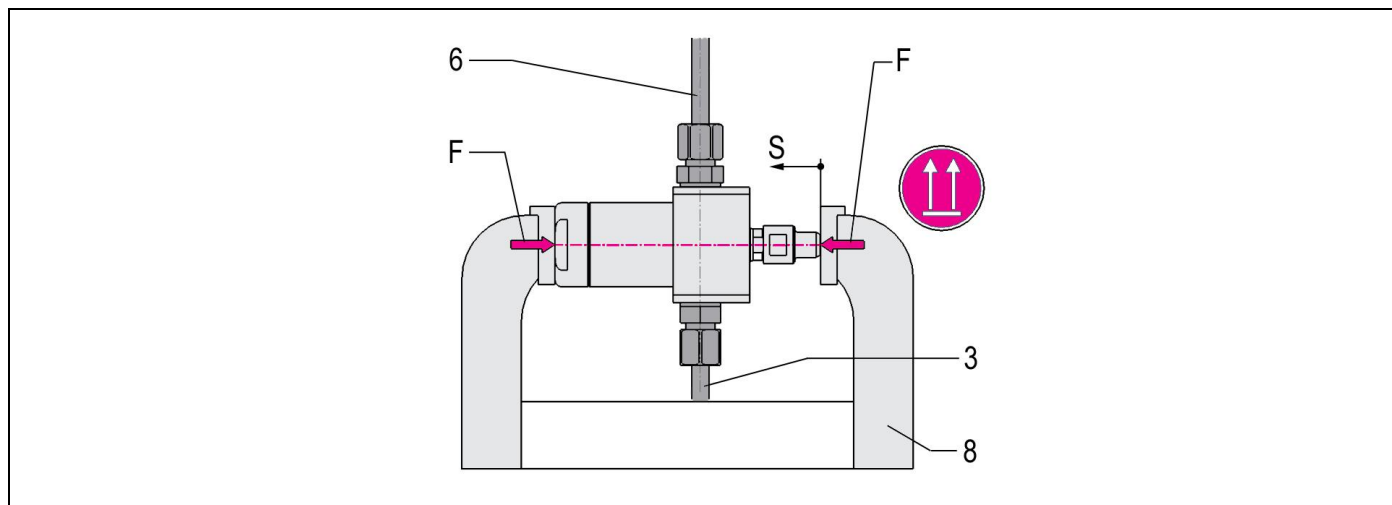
Orientamento per il montaggio senza bolle del collegamento a vite
